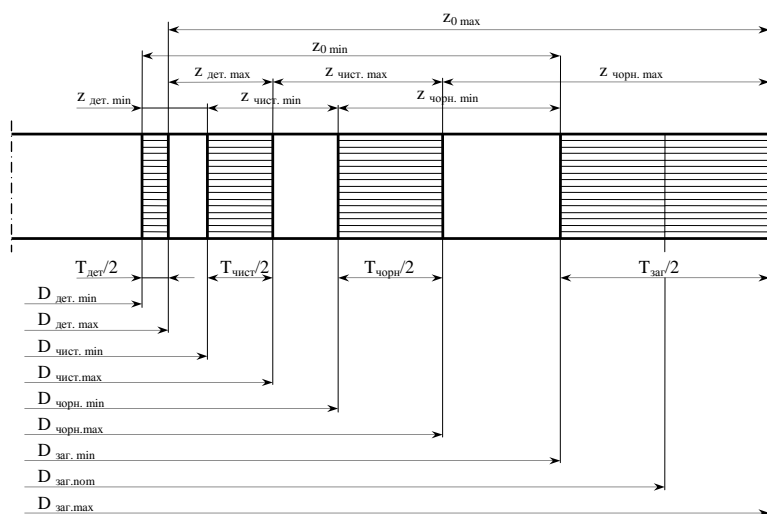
Схема розміщення припусків і допусків на оброблення вала на попередньо налагоджених верстатах
